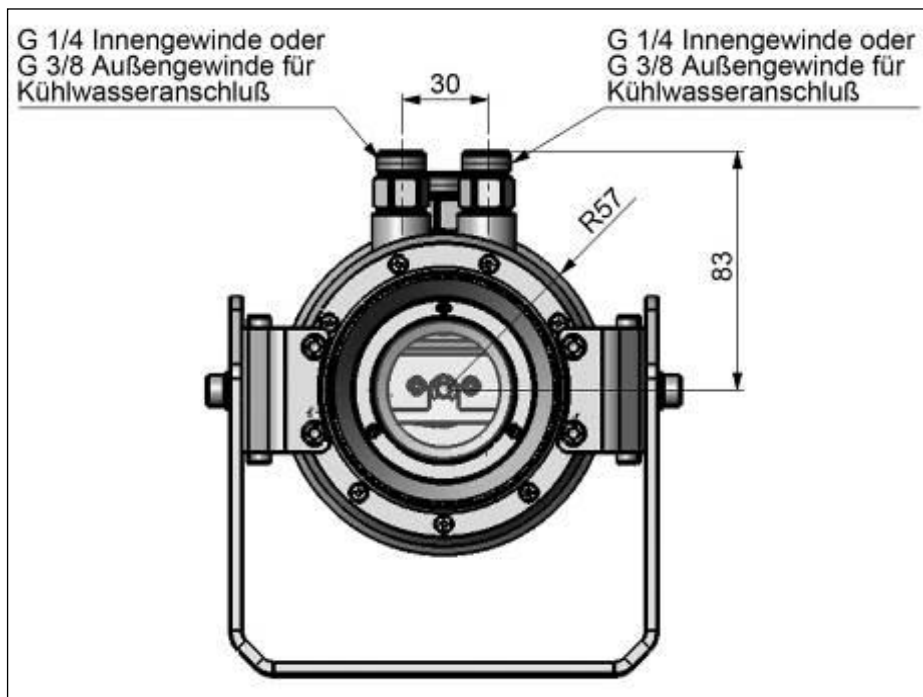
CoolingJacket Advanced, Standard-Version – Seitenansicht
